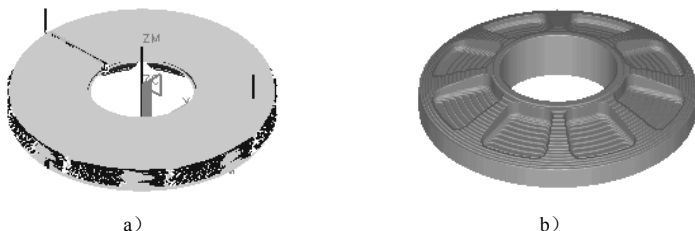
型腔铣粗加工的“刀具路径”和“实体切削验证”
